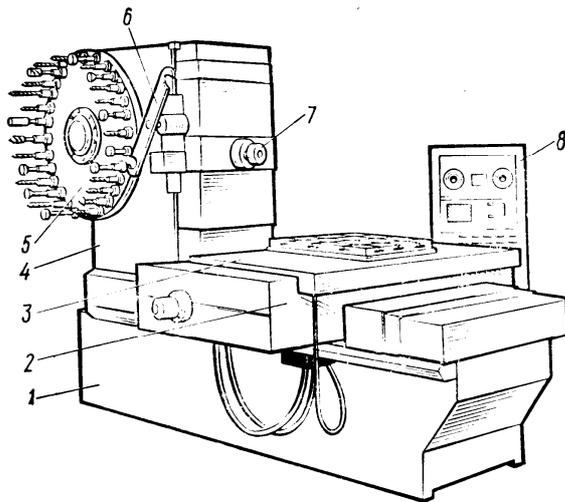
Горизонтальный фрезерно-сверлильно-расточной станок мод. 6906ВМФ2:
